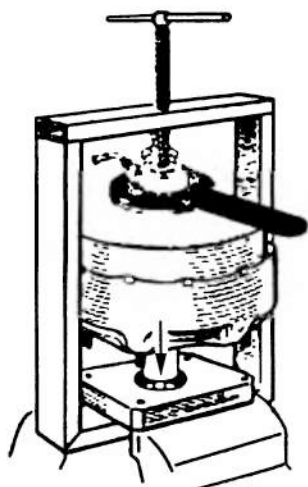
Приспособление для разборки—сборки гидровакуумного усилителя
